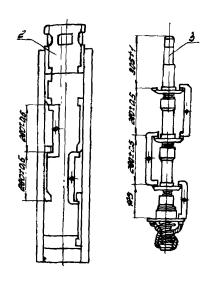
Шаблон для проверки правыдьности установки контактов камеры и схема проверки:
